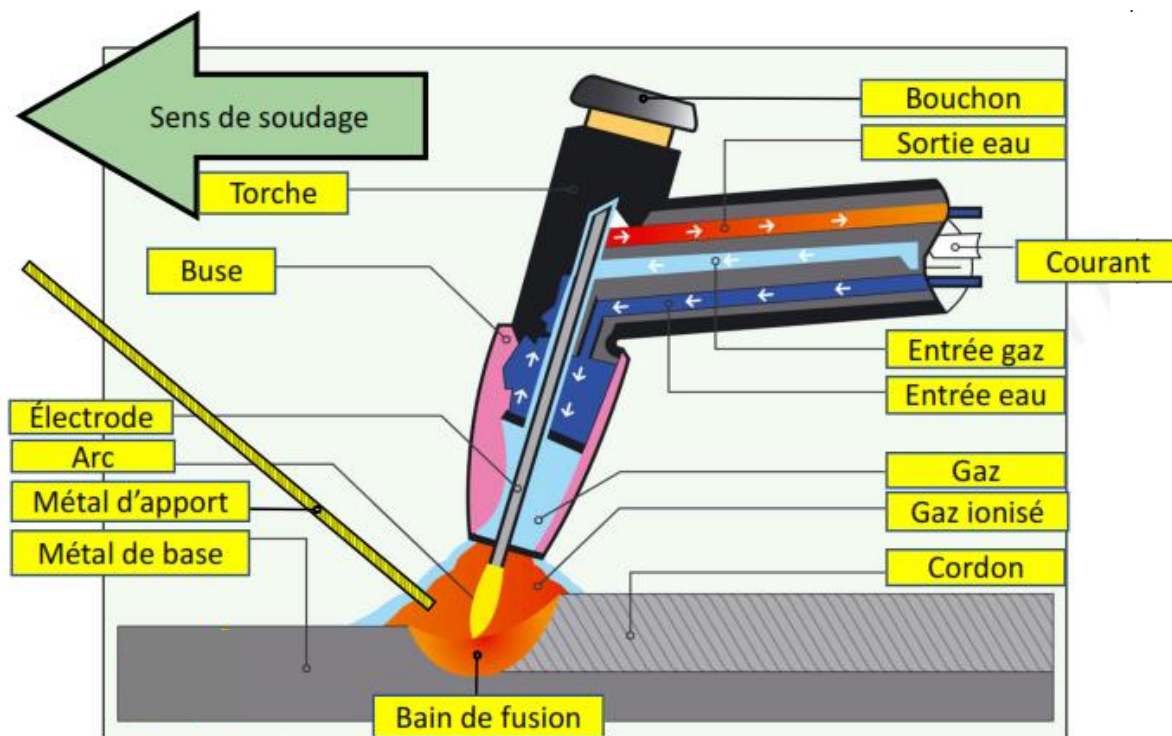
Schéma de principe du soudage TIG.
